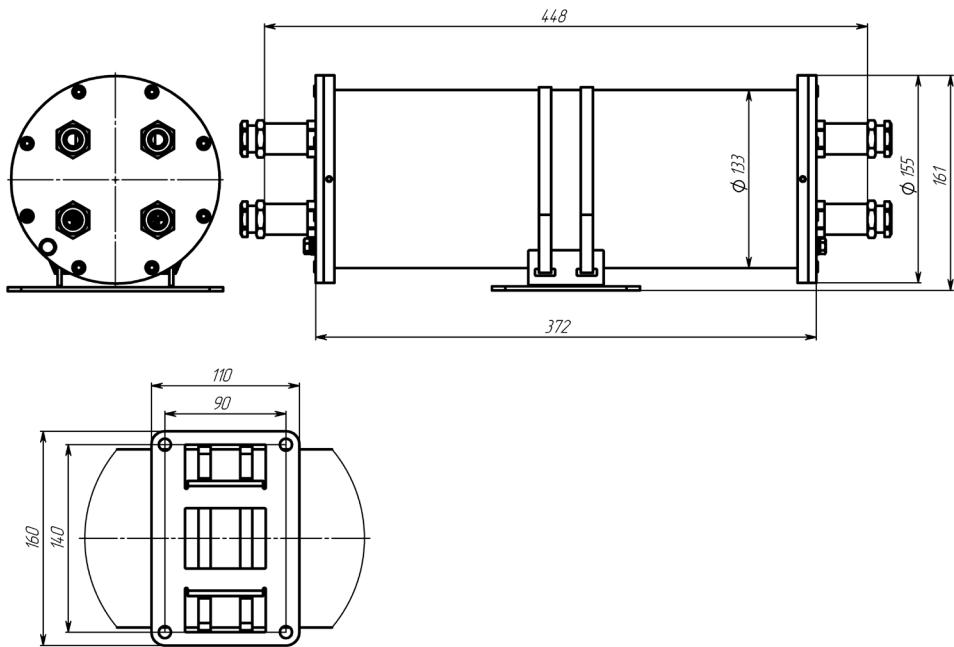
Внешний вид УС-07-Х2-Х3Х4-Р6-Х6-М4XXX-Х8-Х9
